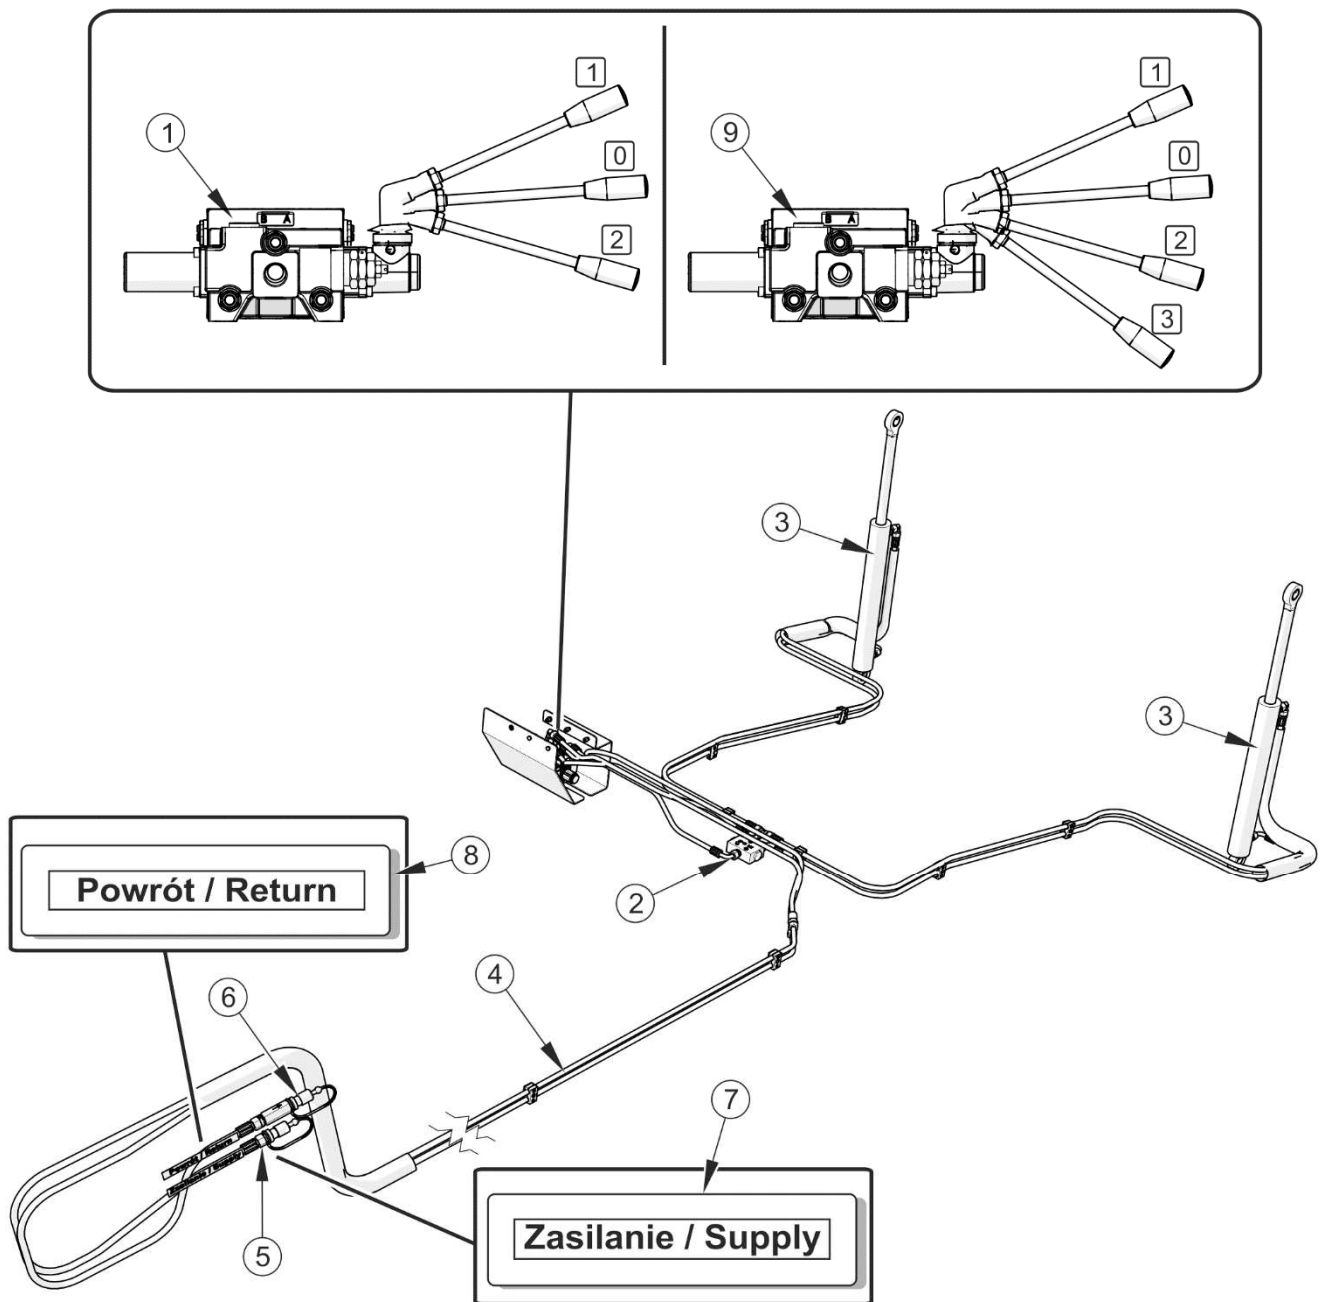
Construction de l'installation hydraulique des rampes
